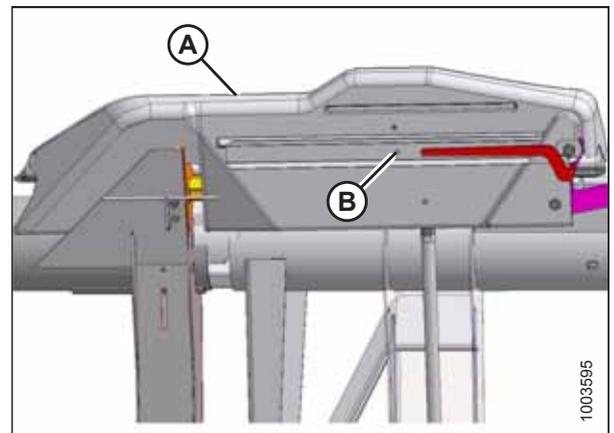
Abdeckung der Schneidwerksmechanik
